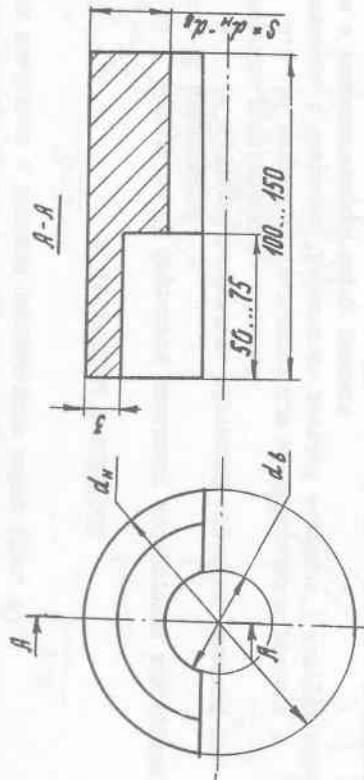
Стандартный образец для настройки ультразвукового прибора при контроле отвода:
